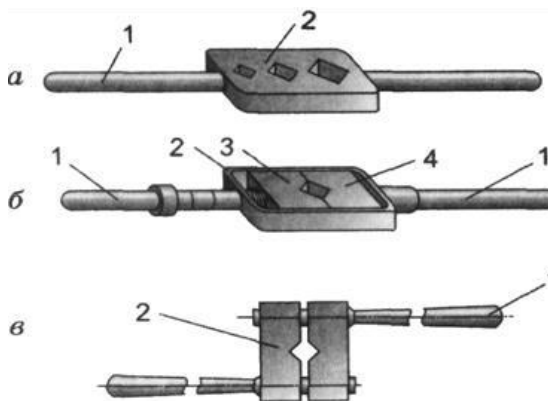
Воротки (метчикодержатели): *а* – цельный; *б* – раздвижной; *в* – разъёмный; 1 – ручка; 2 – корпус; 3, 4 – вкладыши
